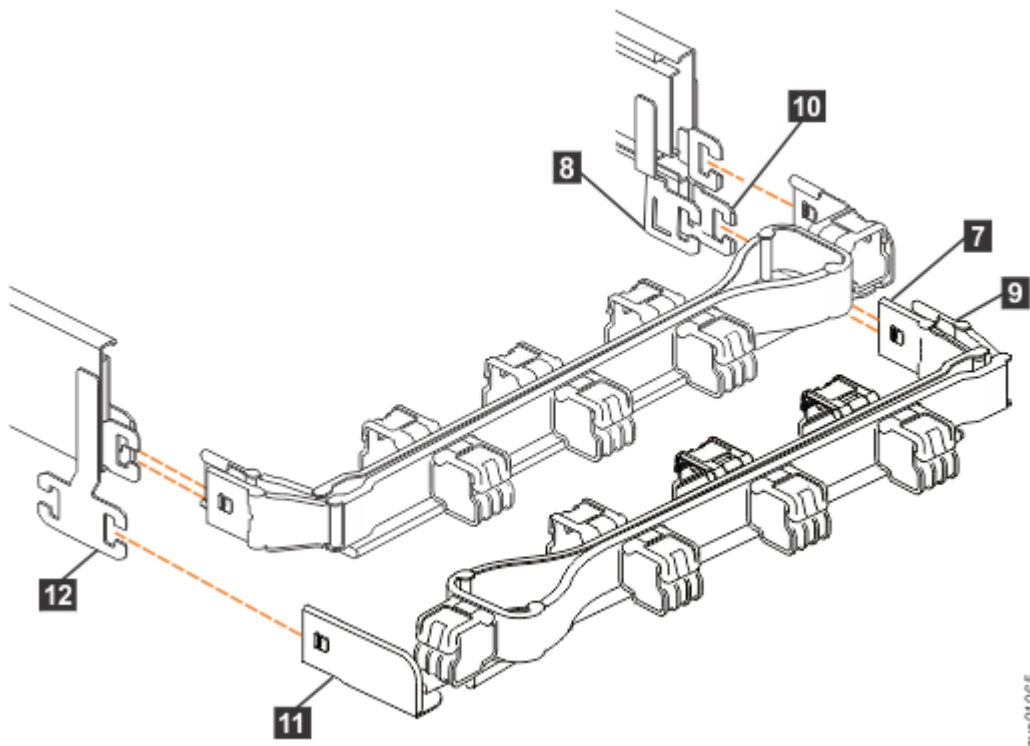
Komponenten der unteren Kabelträgerbaugruppe
